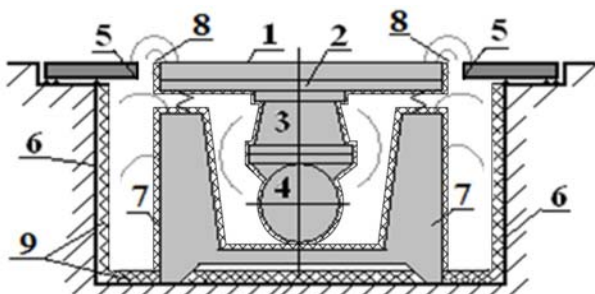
Принципиальная схема камерно-экранный глушителя в приялке под вибро агрегатом:
